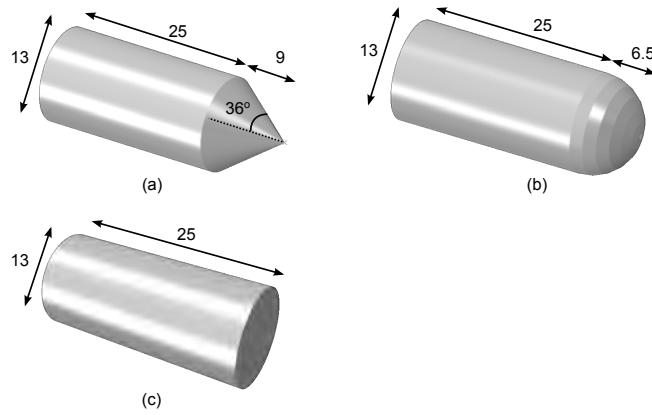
Geometría y dimensiones (mm) de los proyectiles empleados en los ensayos de perforación. (a) Proyectil de punta cónica. (b) Proyectil de punta hemisférica. (c) Proyectil de punta plana.
